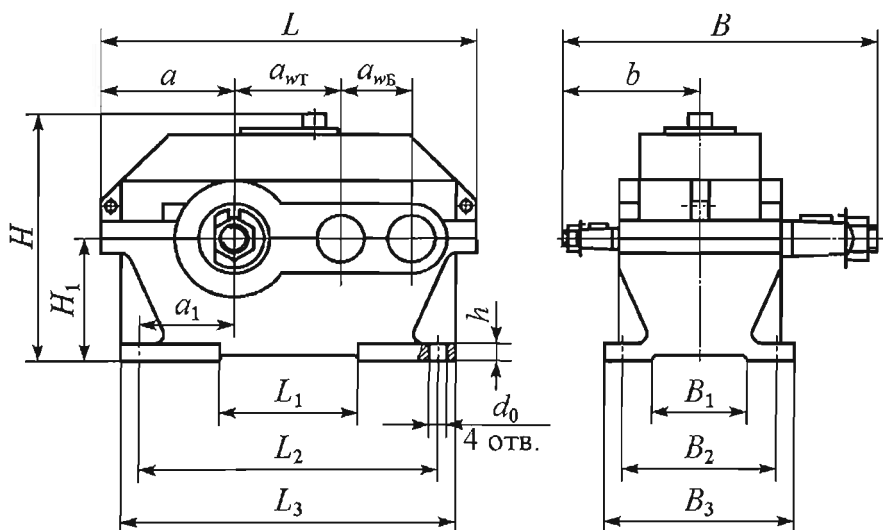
Габаритные, установочные и присоединительные размеры редуктора
